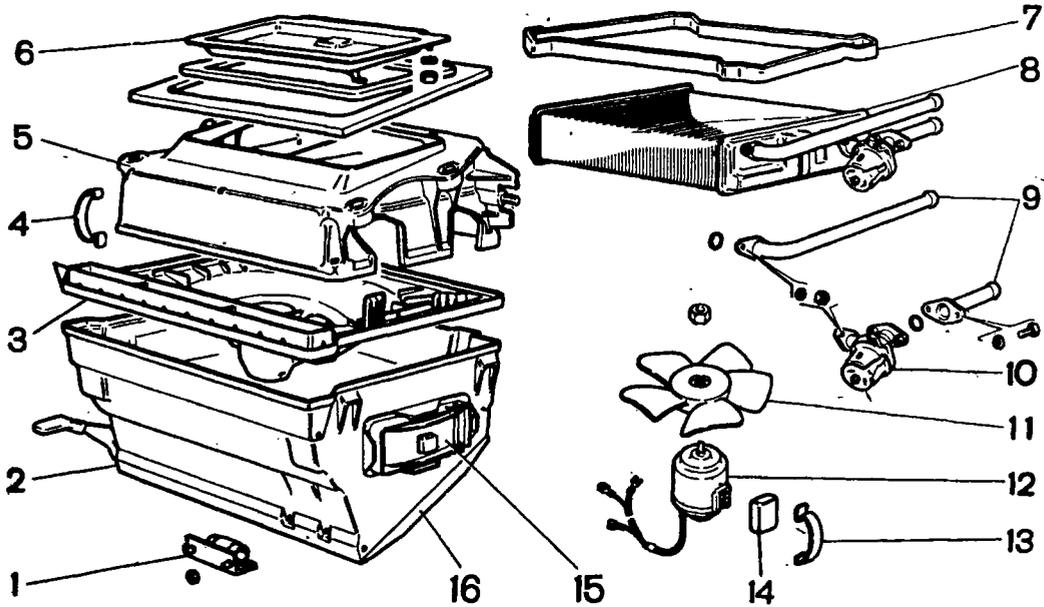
Детали отопителя: 1 - дополнительный резистор; 2 - кожух вентилятора; 3 - кожух направляющий вентилятора; 4 - пружинные держатели кожуха вентилятора; 5 - кожух радиатора; 6 - крышка воздухопритока; 7 - крышка радиатора; 8 - радиатор; 9 - патрубки; 10 - кран; 11 - крыльчатка; 12 - электродвигатель; 13 - пружинный держатель вентилятора; 14 - подушка электродвигателя; 15 - заслонка; 16 - воздухораспределительная крышка
